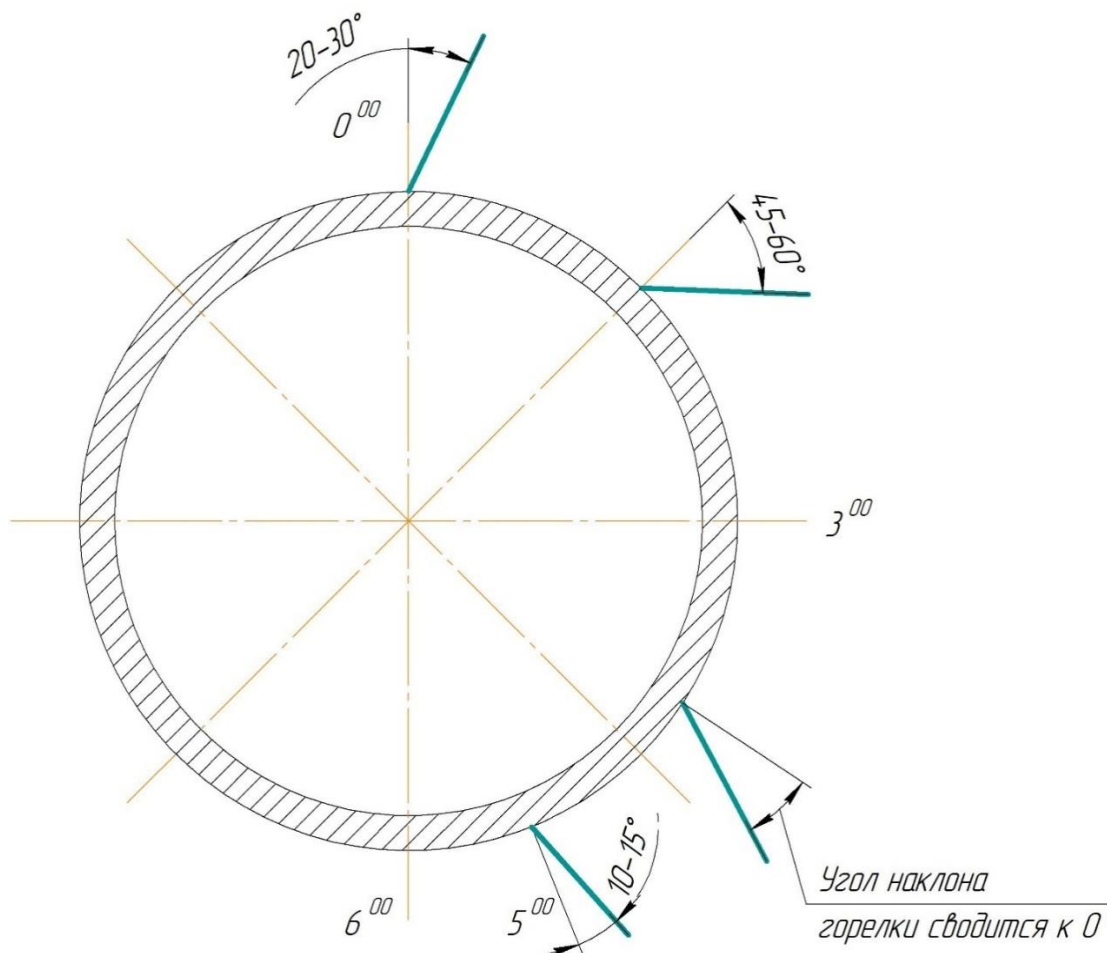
Изменение угла наклона сварочной горелки при механизированной сварке самозащитной порошковой проволокой неповоротных кольцевых стыковых соединений труб
